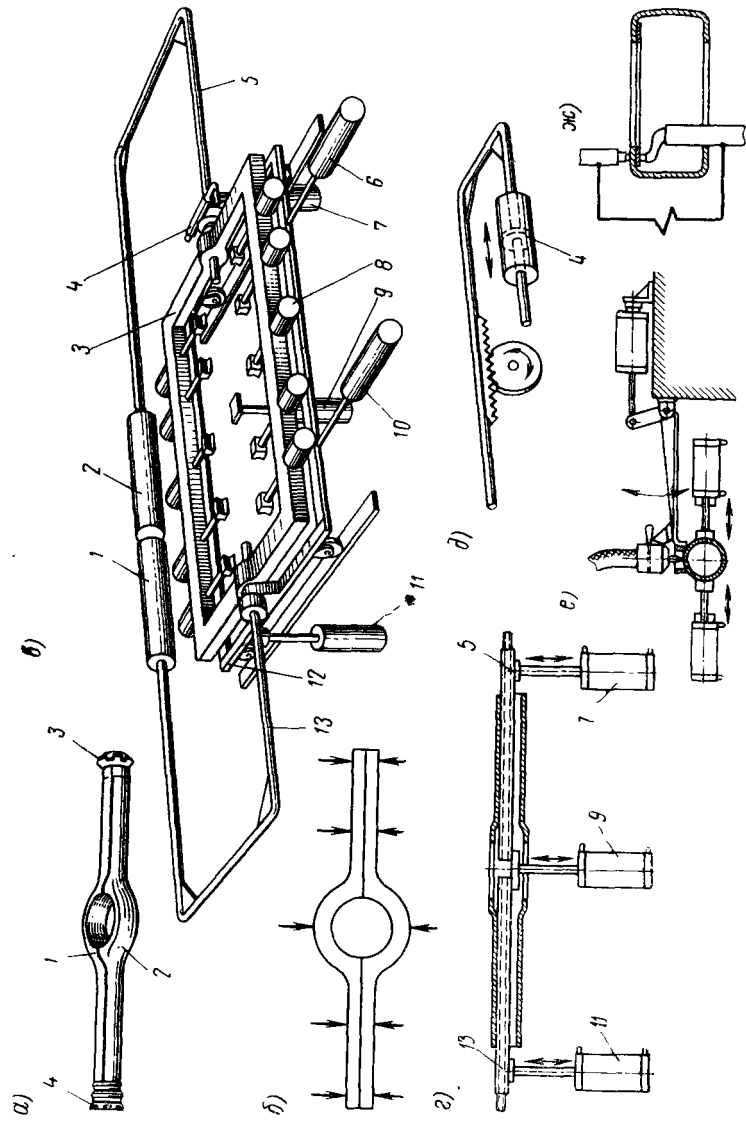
Балка заднего моста автомобиля «Москвич» модели 407 и схема устройств для сварки
